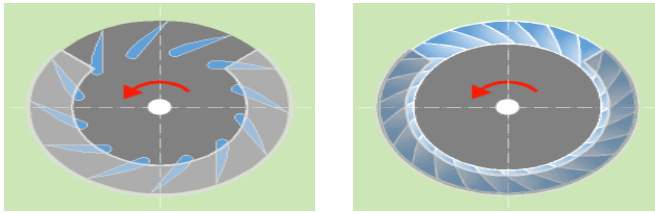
Roue de ventilateur centrifuge à aubes inclinées vers l'arrière (double ouïe) [2].
